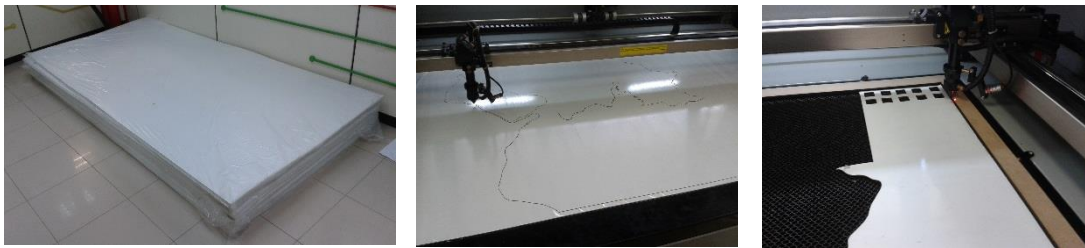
27 Planchas pvc Fab-Lab UTPL
